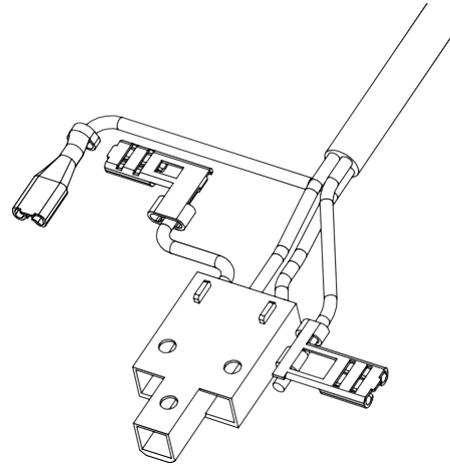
Cable del motor para la serie de compresores VNE con OLP
